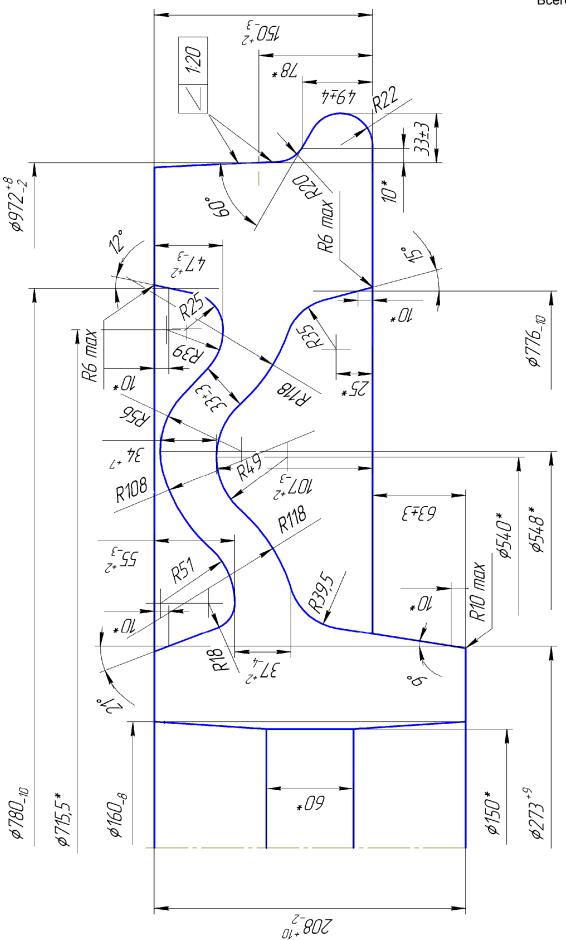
Колесо без механической обработки Ø 972 мм под Ø 950 мм, черт. №КР-0040-16. Масса чернового колеса на 2/3 поля допуска = 594 кг.
